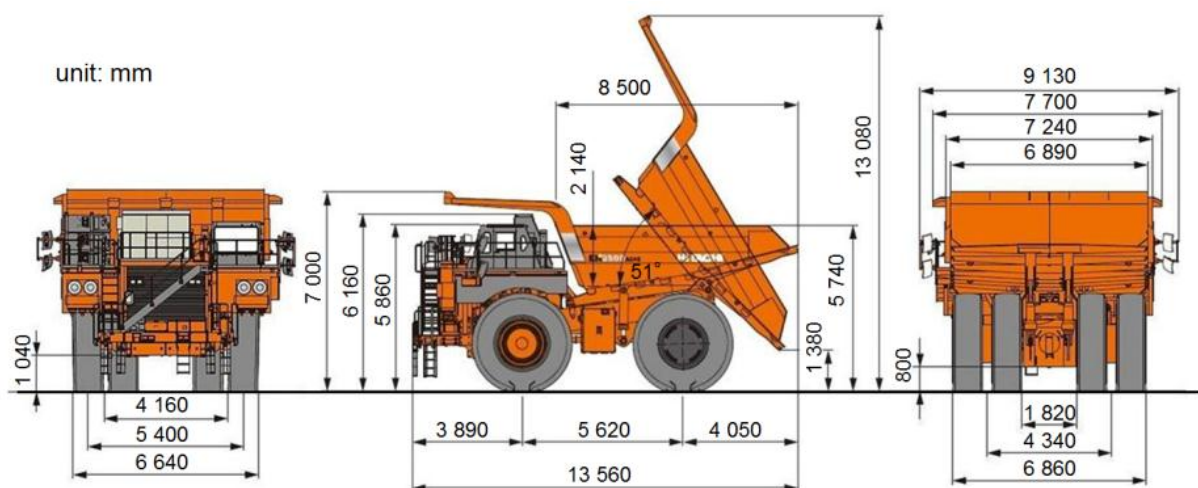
dimensions du camion HITACHI EH3500AC-3.
